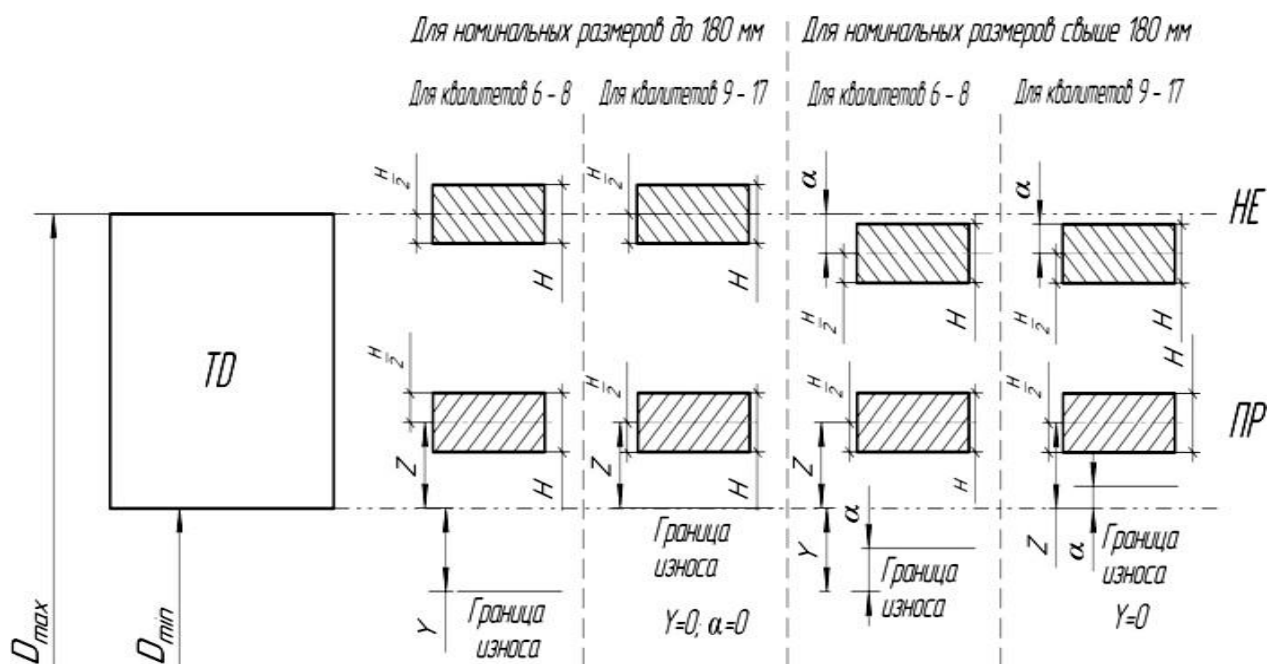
Схема расположения полей допусков калибров для контроля отверстий
